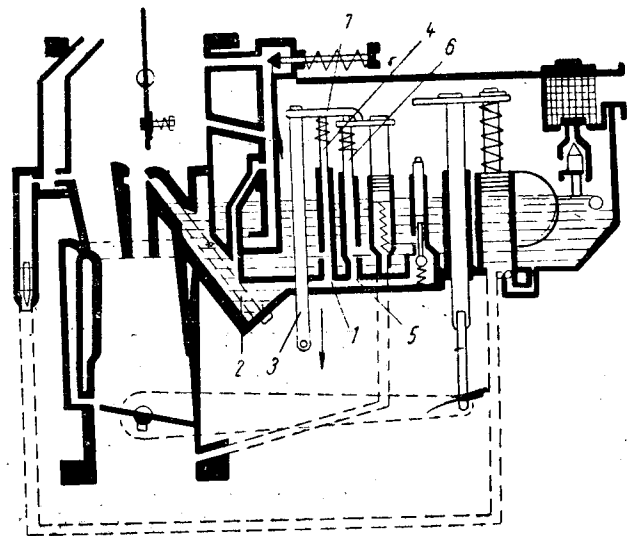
Схема карбюратора К-82 с устройством для прекращения подачи топлива
